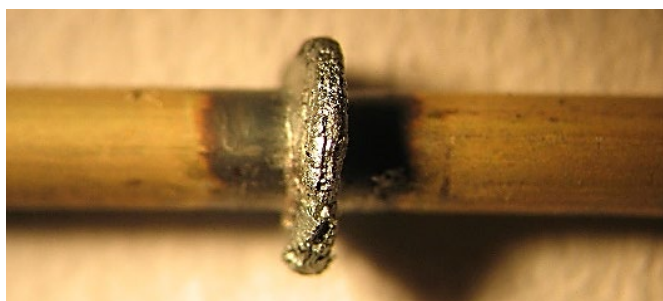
Внешний вид сварного соединения с гратом латунированной проволоки после стыковой сварки сопротивлением, $\times 6$
